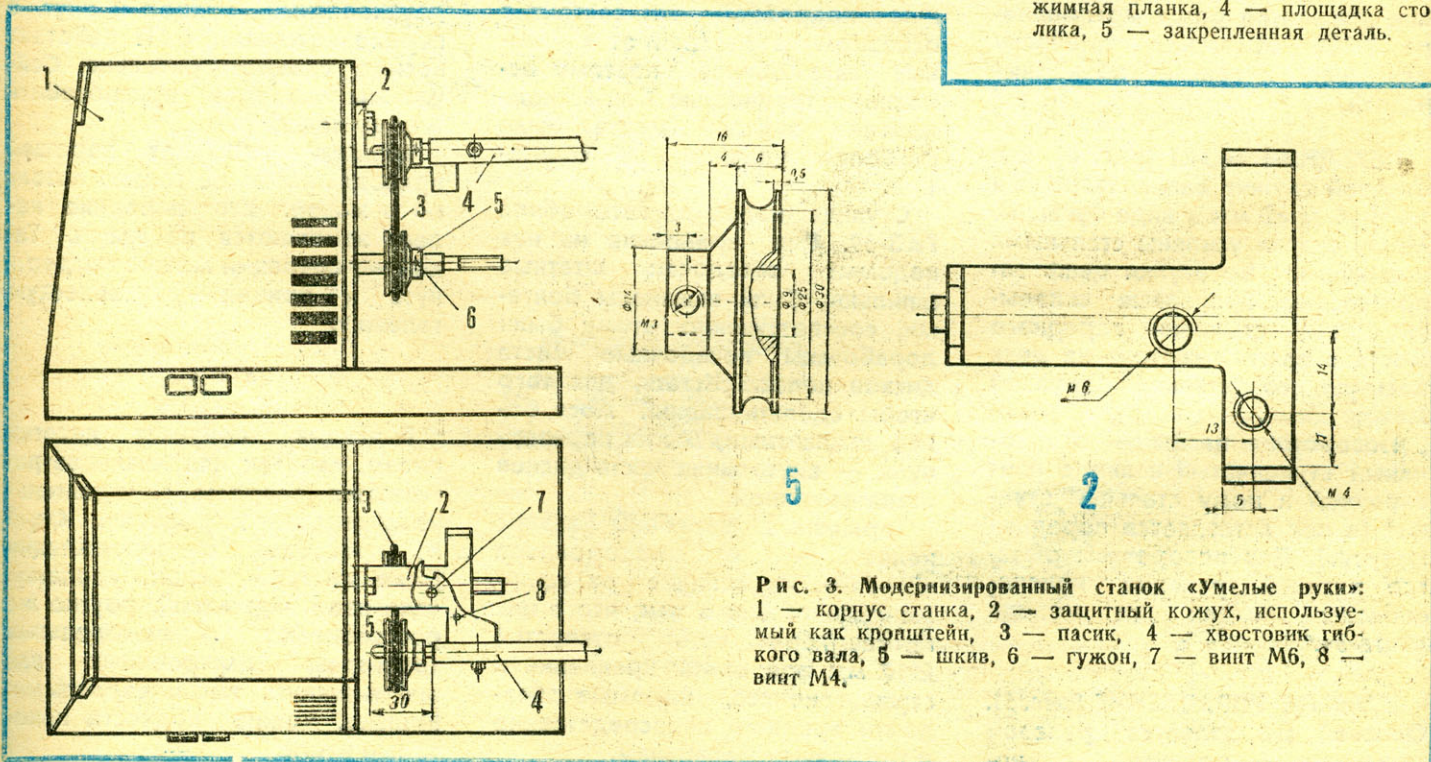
Модернизированный станок «Умелые руки»: 1 — корпус станка, 2 — защитный кожух, используемый как кронштейн, 3 — пасик, 4 — хвостовик гибкого вала, 5 — шкив, 6 — гужон, 7 — винт М6, 8 — винт М4.
